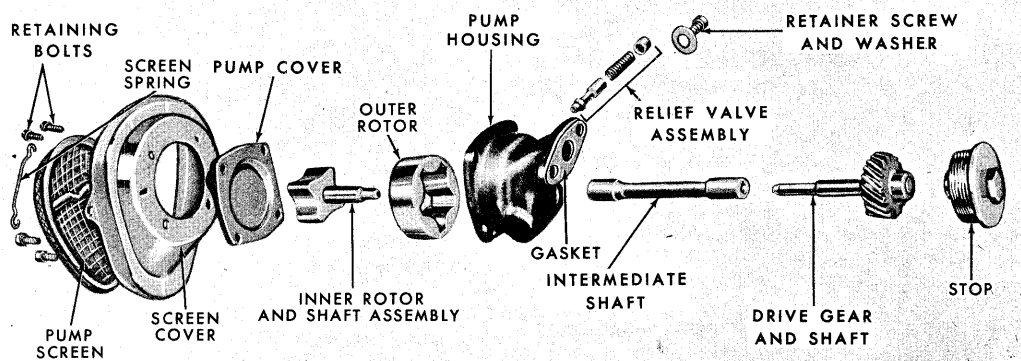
Exploded view af olie pumpen med si, reduktionsventil, aksel og drev.
